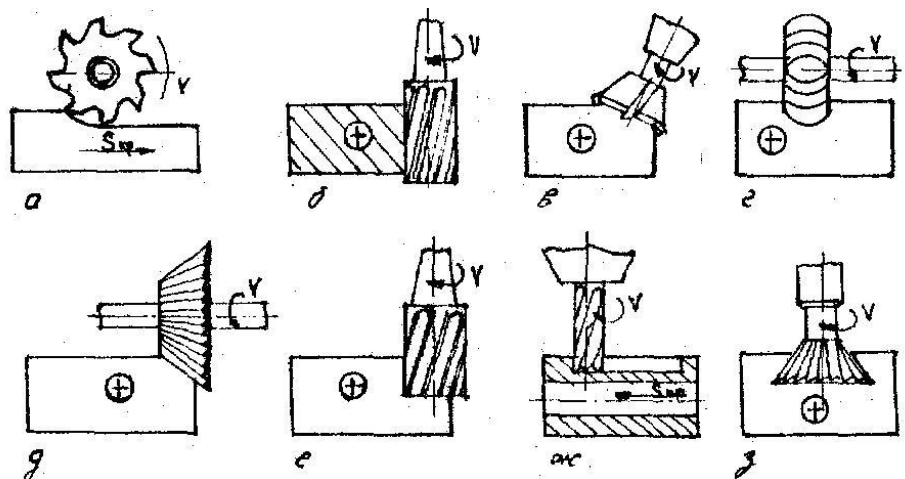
Схеми обробки заготовок на фрезерувальних верстатах
